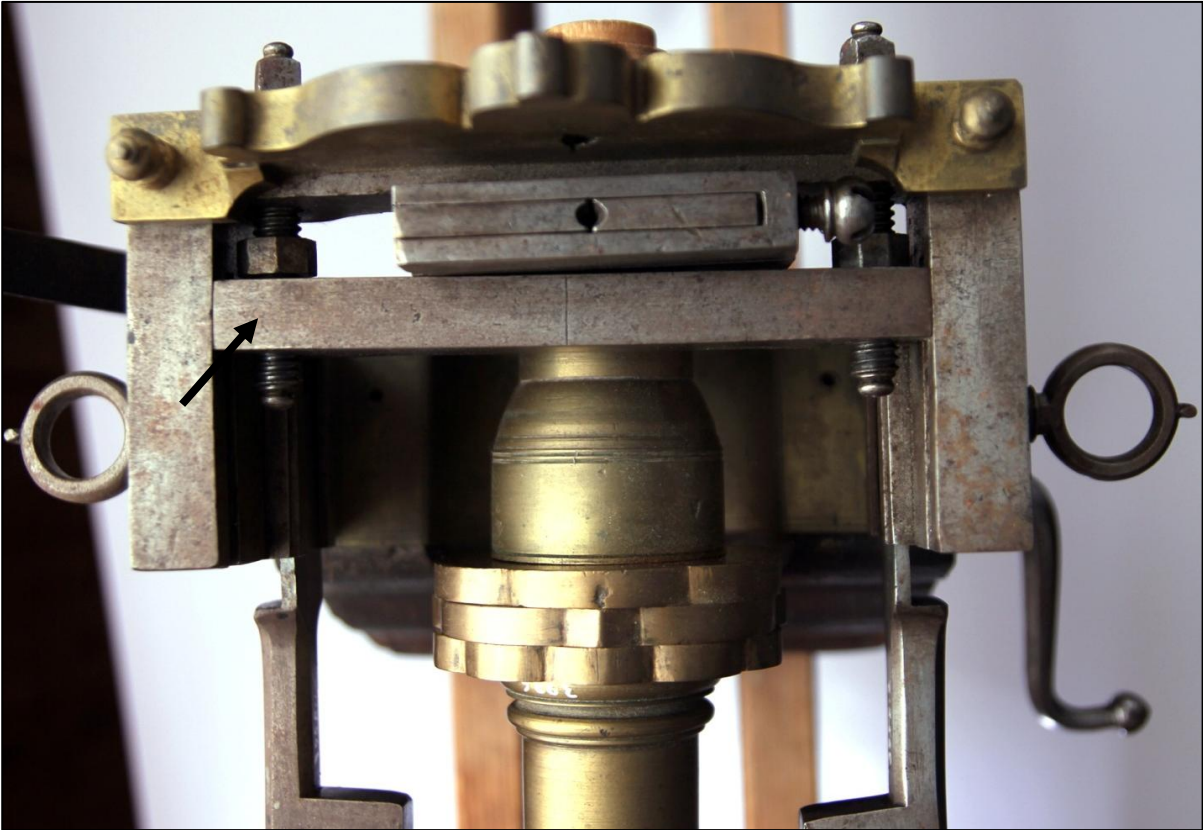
Spindeldok nr. 3942, spindel med monterede rosetter
